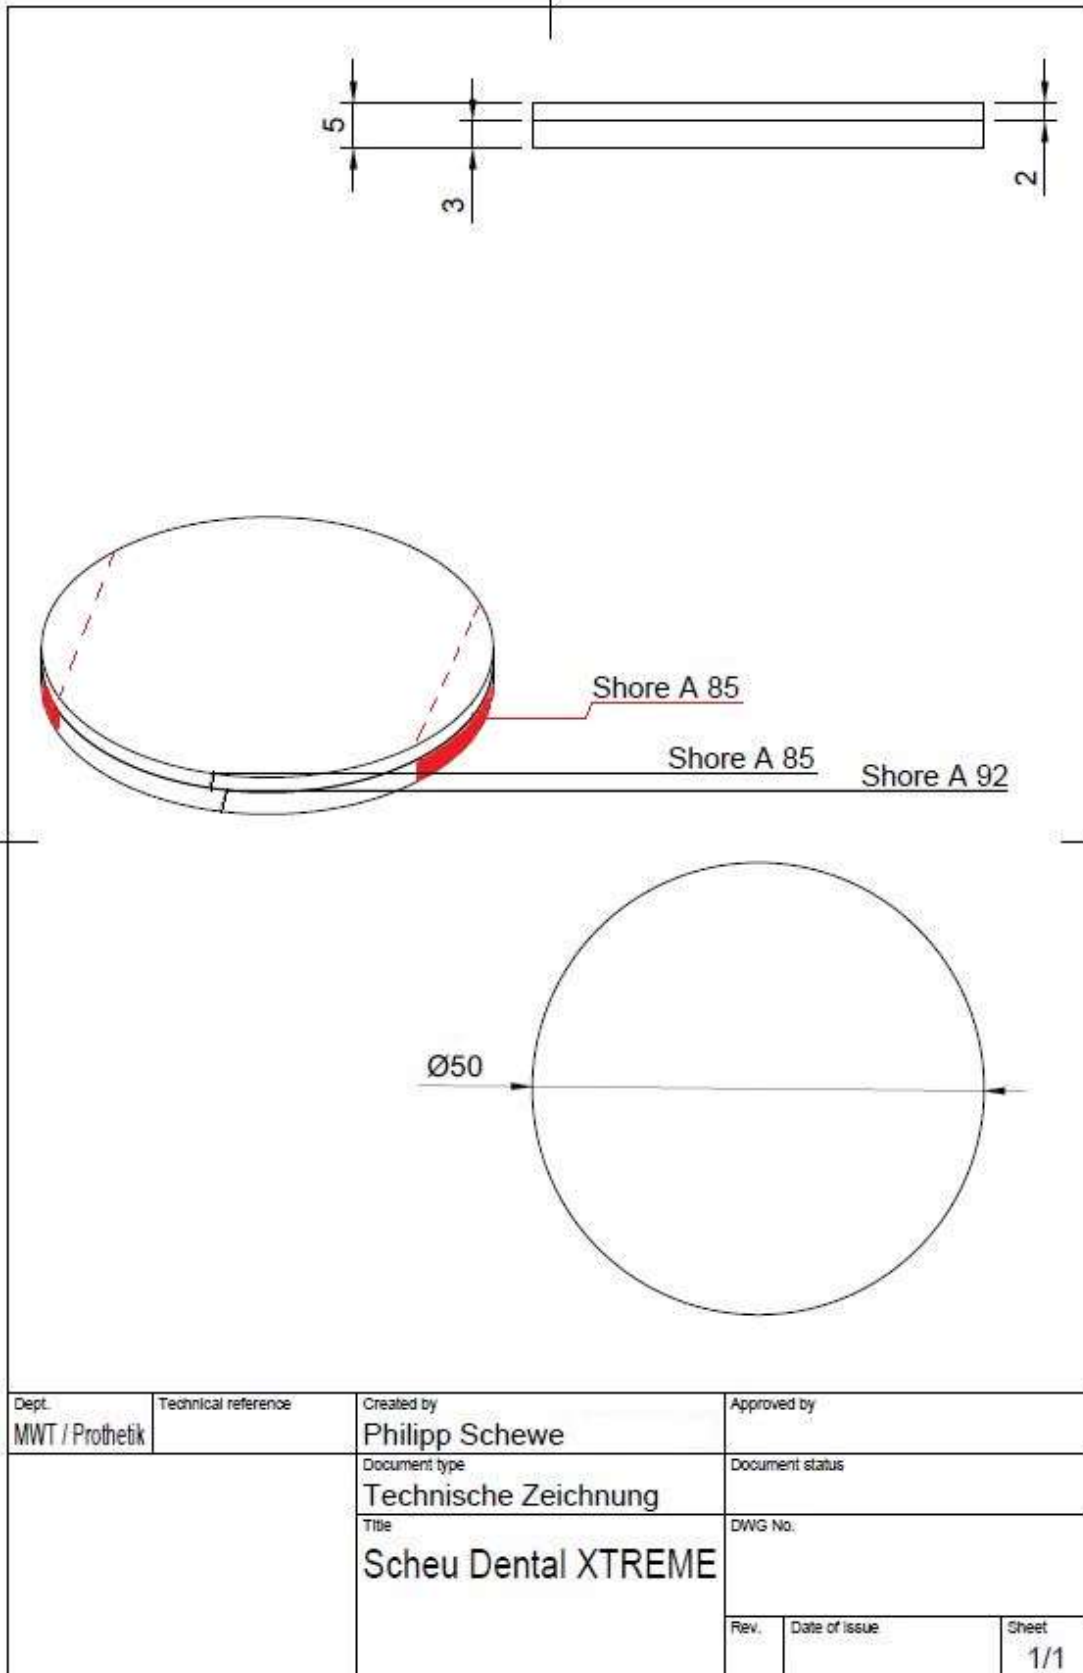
Technische Zeichnung der Materialprobe SCH-Xtr / STR-B
